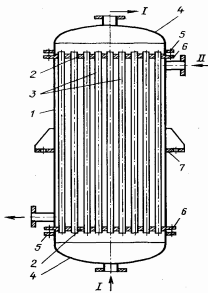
Кожухотрубний теплообмінний апарат одноходовий безперервної дії: 1 — корпус або кожух; 2 — трубні решітки; 3 — труби; 4 — днища і кришки розподільчих камер; 5, 6 — фланці; 7 — опори
